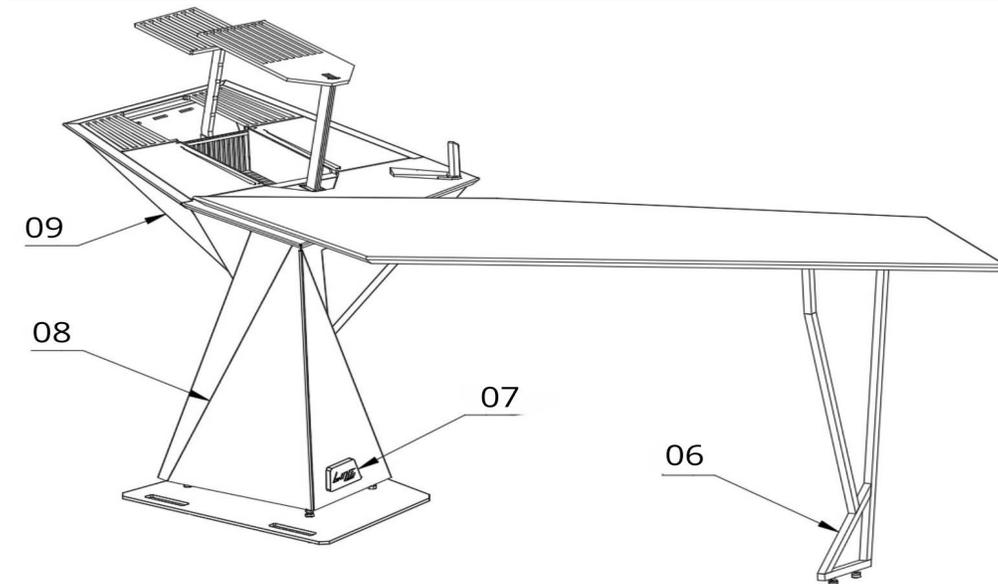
Vue d'ensemble – Perspective arrière gauche
